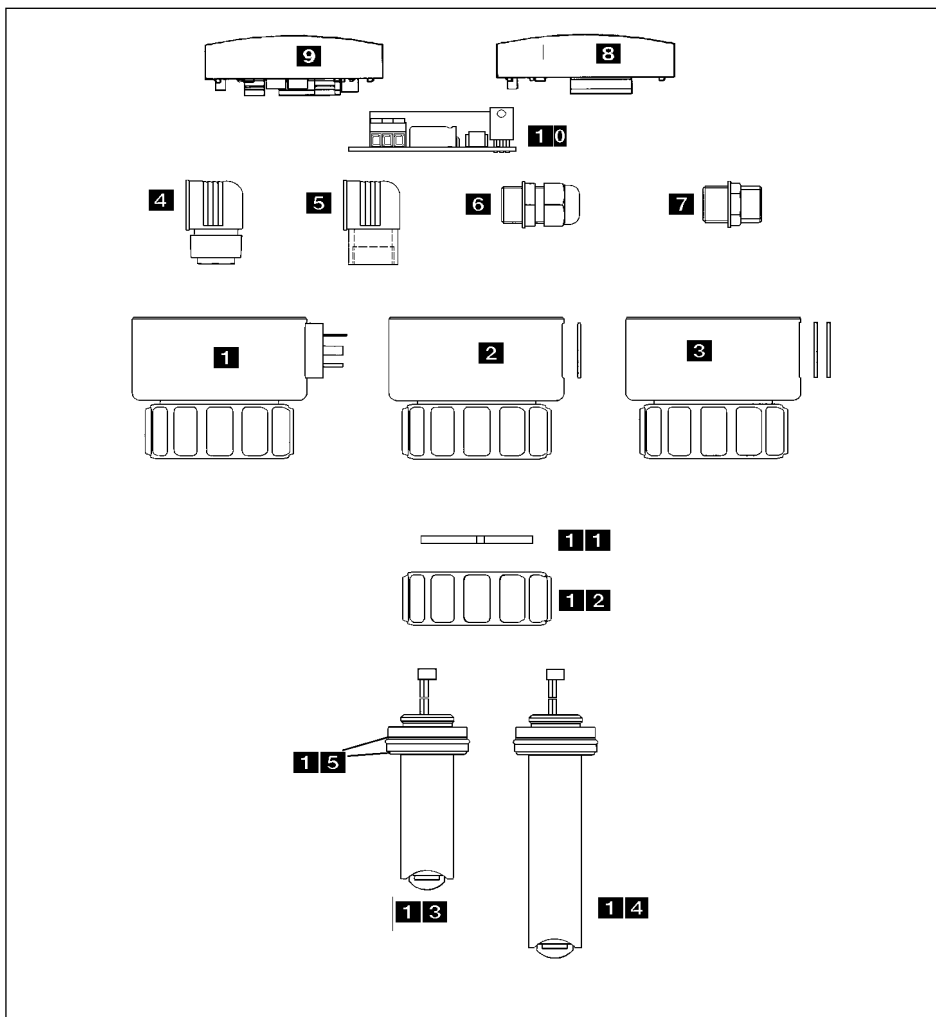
Vue éclatée des pièces de rechange 8025 version compacte
